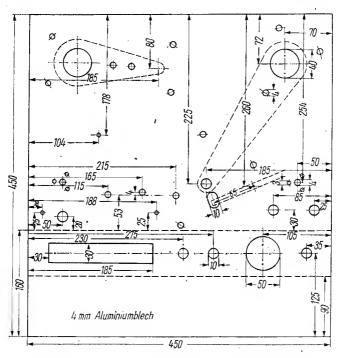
Chassisplatte - Das Chassis wird aus 4 mm Alu gebogen
